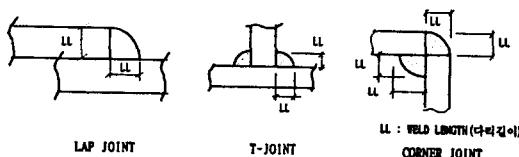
c(1) FILLET WELD의 종류(형태)
